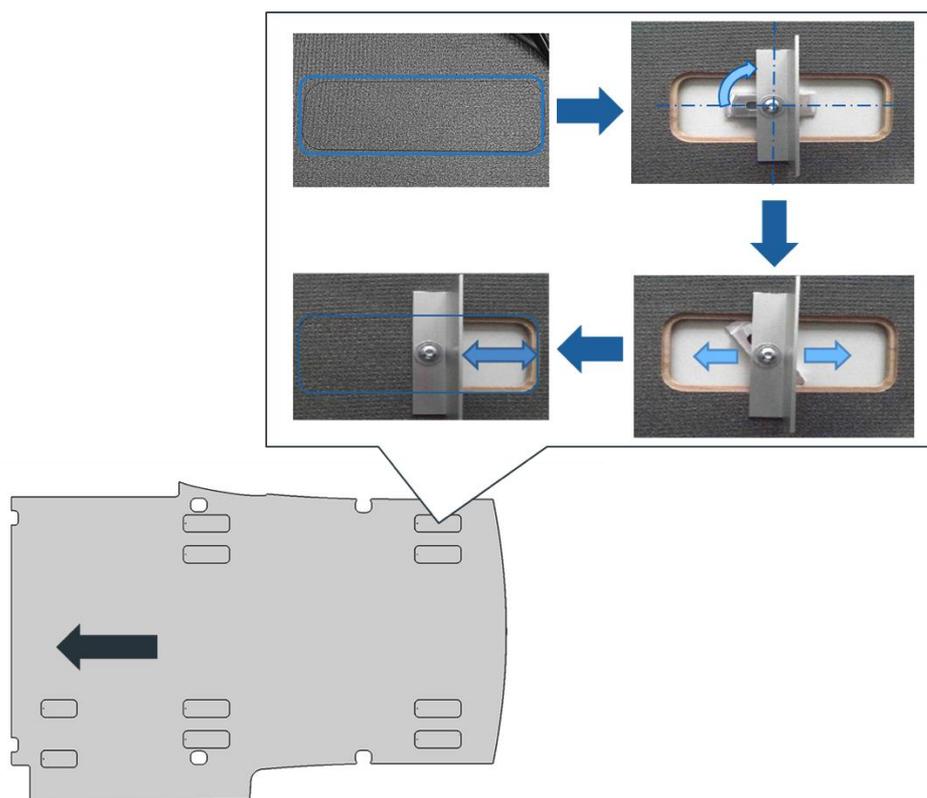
plancher universel (5BM)- Points de fixation pour systèmes d'armoires et d'étagères (Représenté : Caddy Maxi avec porte coulissante droite)
